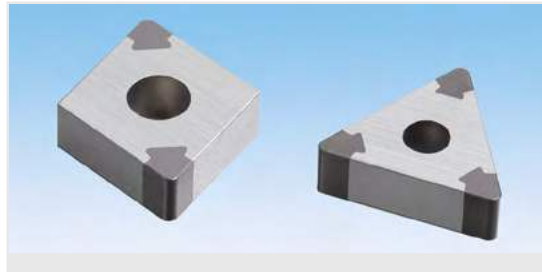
Schneidplatten mit eingelöteten CBN-Segmenten
